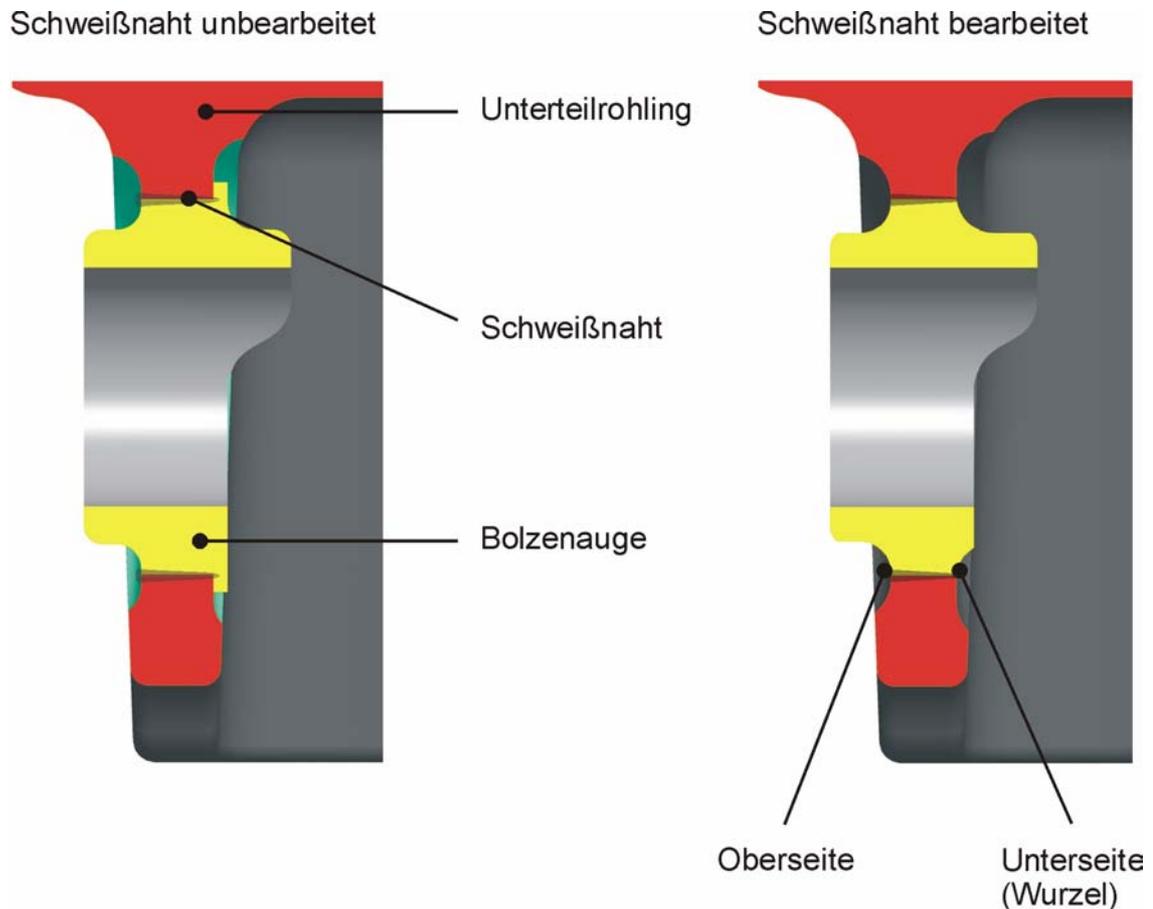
Schweißnahtbearbeitung auf der Innen- und Außenseite des Schaftes
